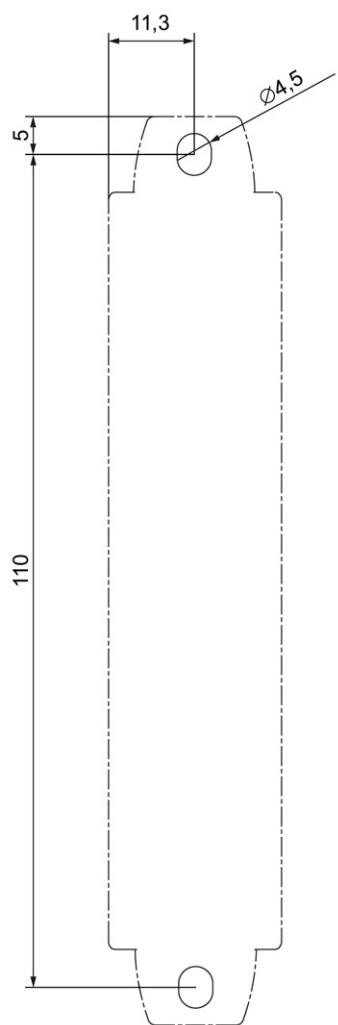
Bohrplan Gehäuse 22,5 mm
